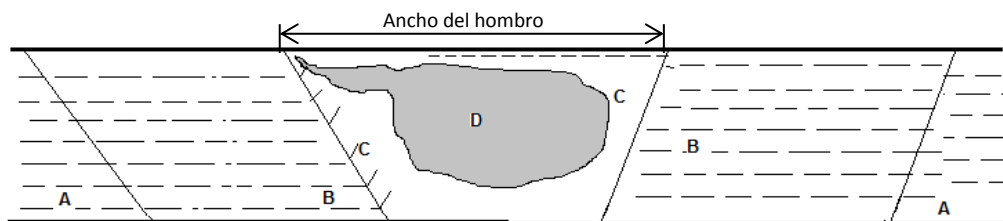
Esquema del proceso de soldadura por fricción agitación [16].
